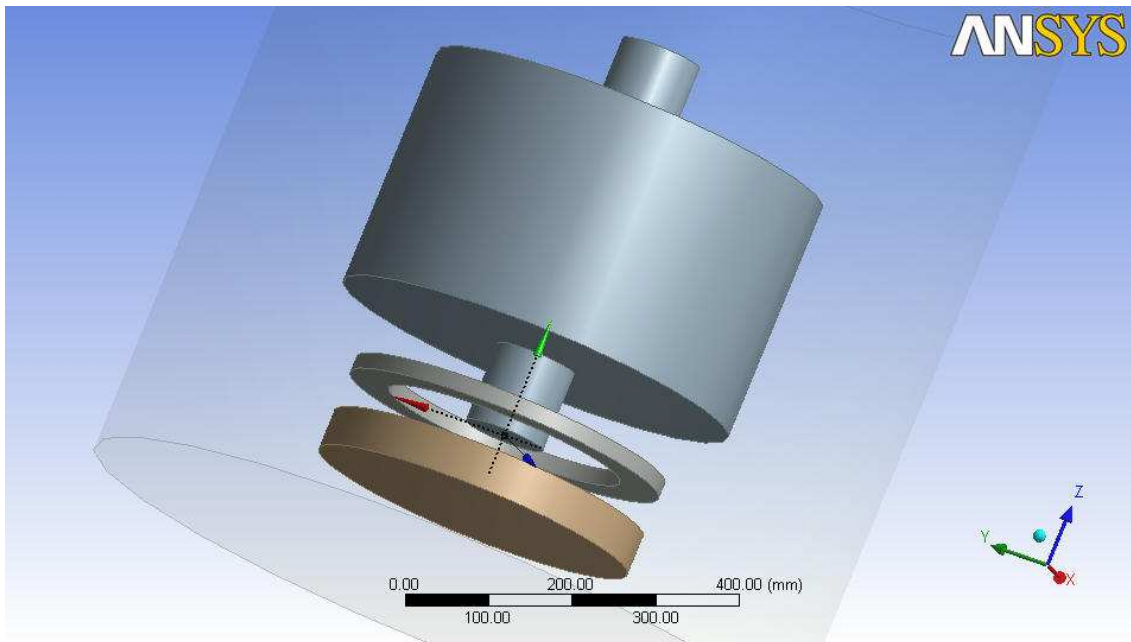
Alçado frontal do conjunto rotor + supercondutor.
